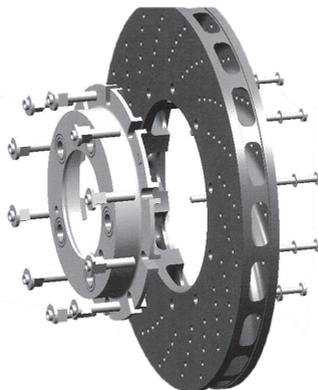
Explosionsdarstellung einer Baugruppe einer keramischen Leichtbaubremsscheibe. [62]
